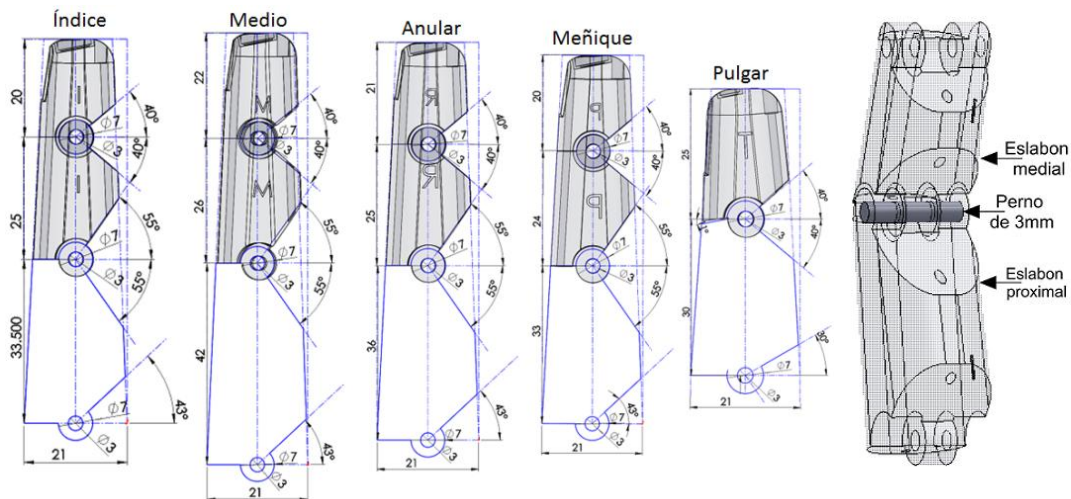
Dimensiones físicas de falanges (En mm.) diseñados y movimiento.
